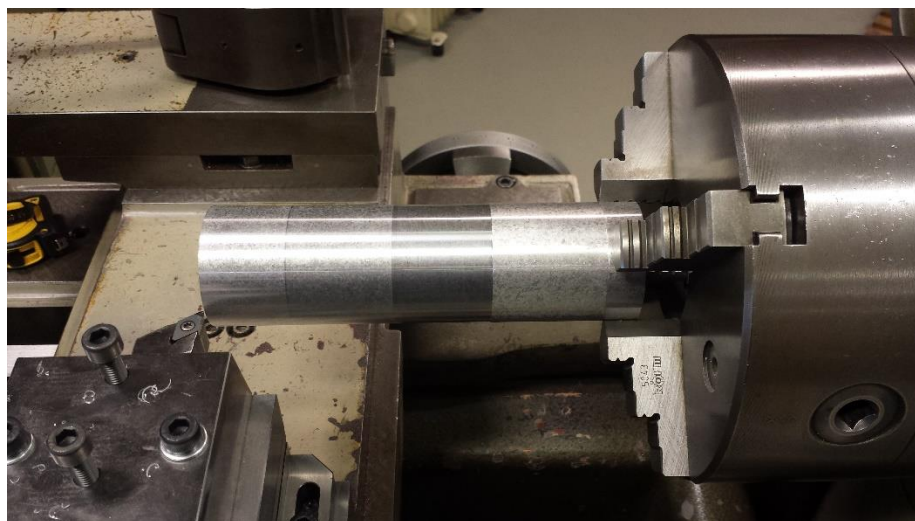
Setup para ensaio de torneamento cilíndrico exterior
